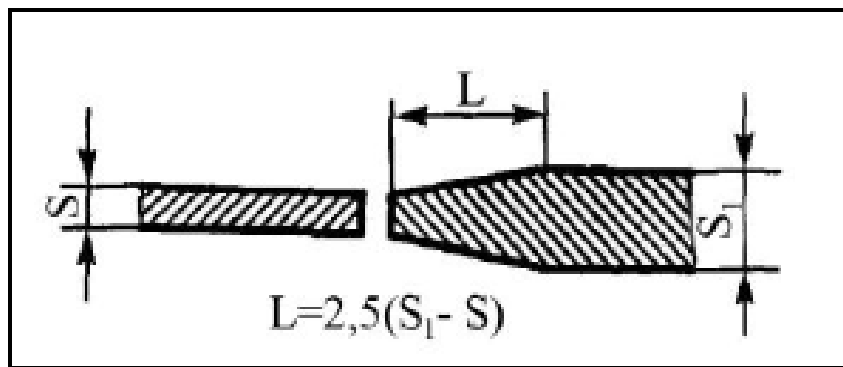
Оброблення кромки для зварювання листів різної товщини:
